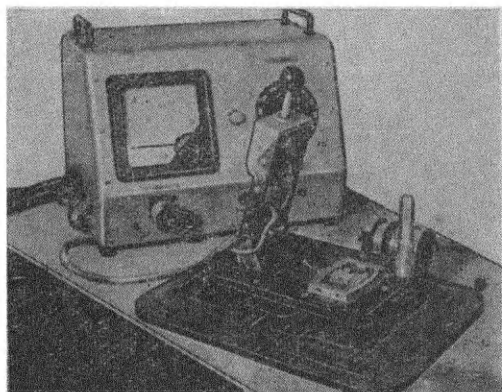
Приспособление для сборки и пайки микромодулей.
